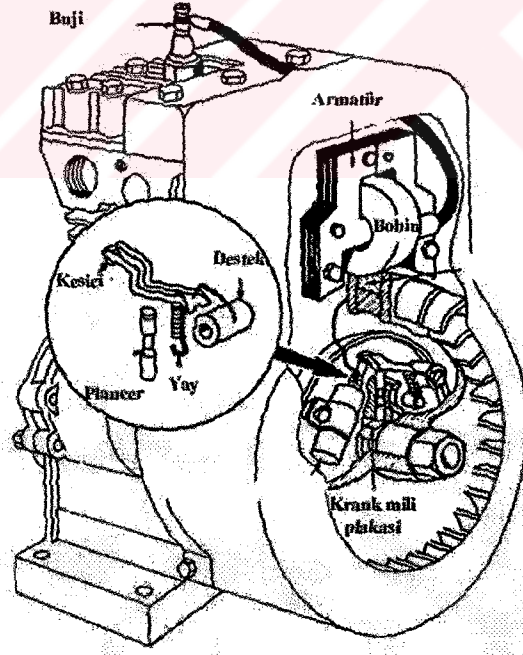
Kıvılcım oluşturmak için seramik magnet kullanımı (Miller & Miller, 1993)
